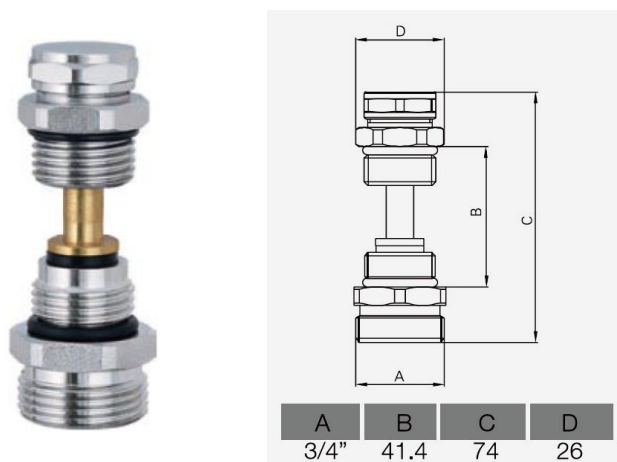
Регулирующая вставка - конструкция и габариты в мм.
